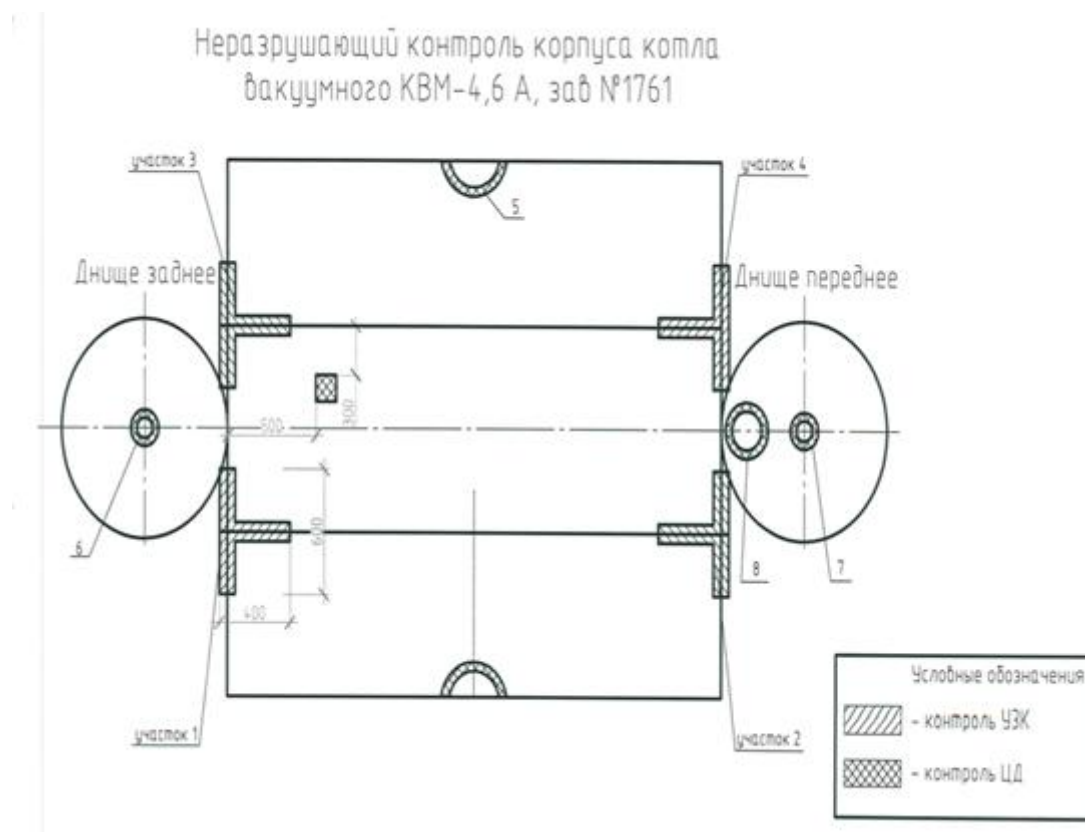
Схема неразрушающего контроля корпуса котла KBM-4,6А
